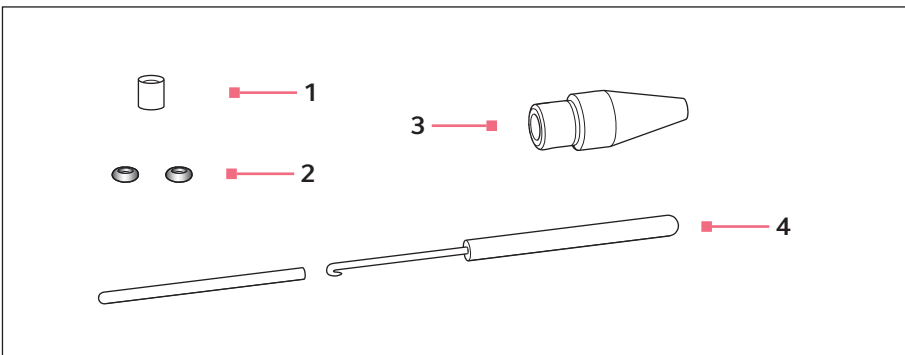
Spannkopf 4 mit Entnahmewerkzeug
